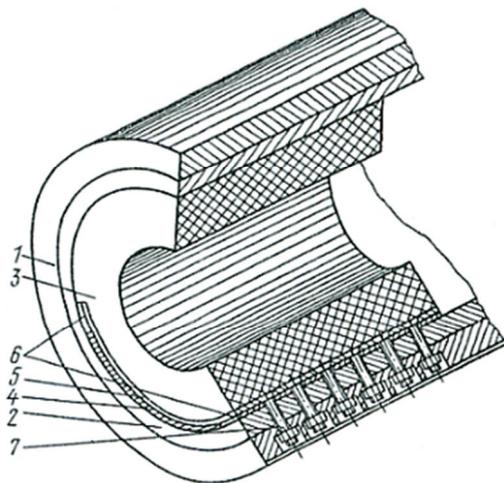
Схема укороченного дейдвудного подшипника: 1 – дейдвудная труба; 2 – промежуточная металлическая втулка; 3 – капролоновый вкладыш; 4 – паз; 5 – упругий элемент; 6 – опорная прокладка; 7 – болт
